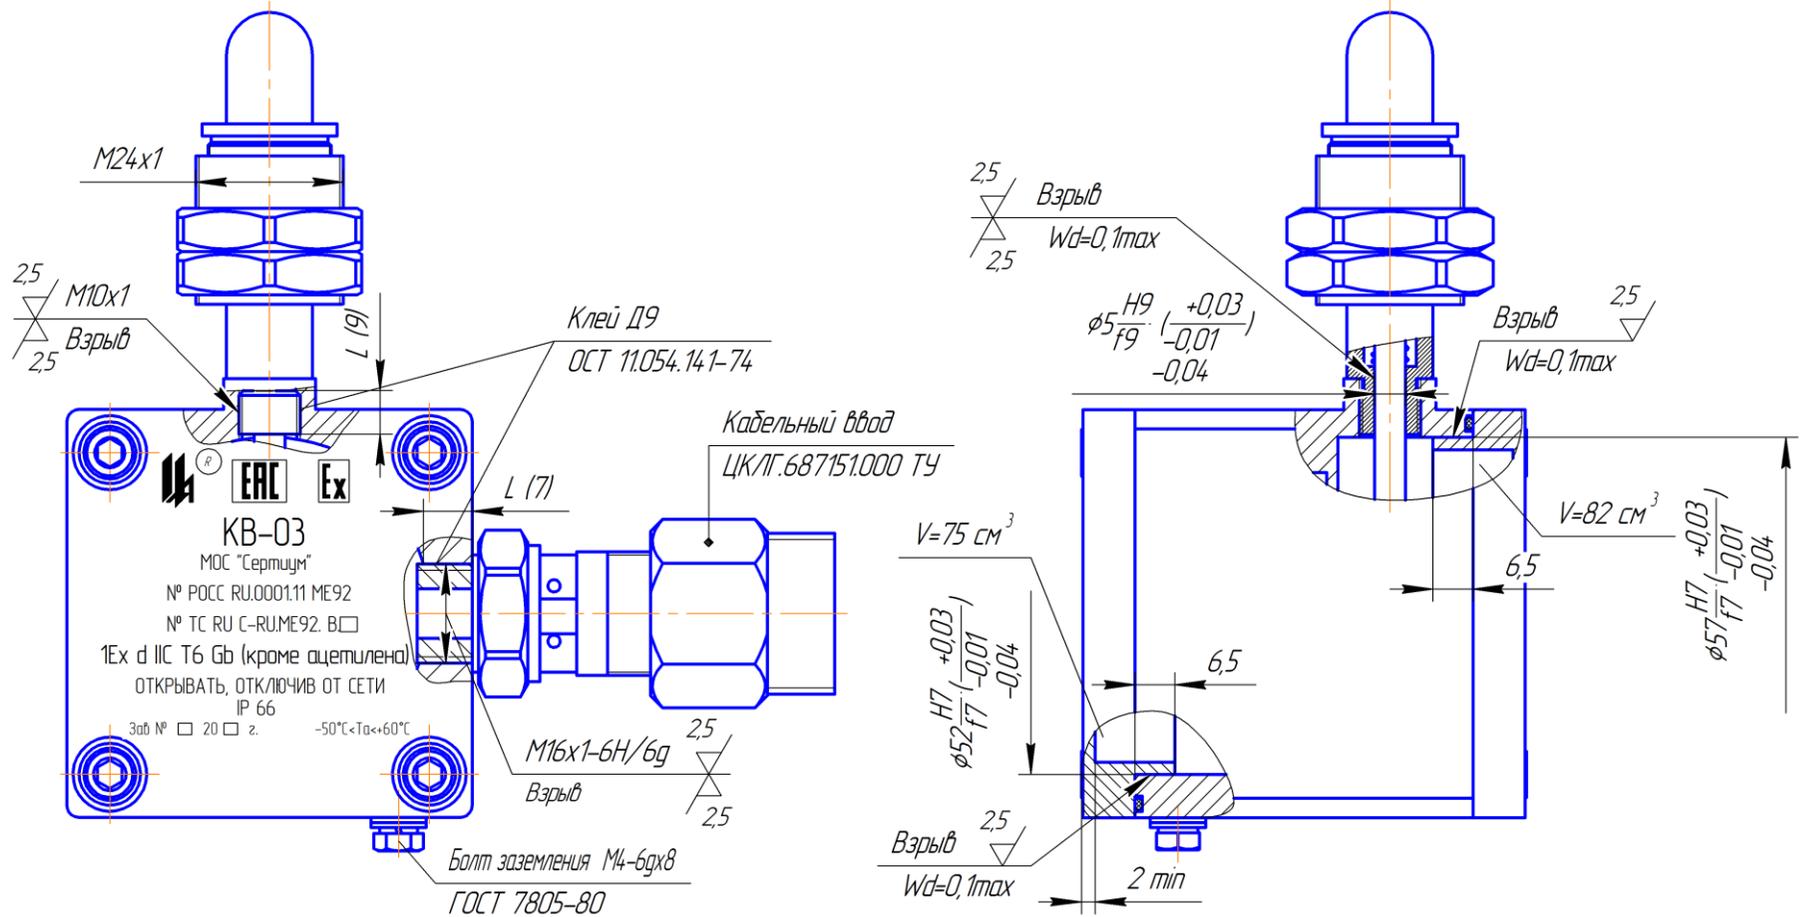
Габаритно-монтажный чертеж KB-03
